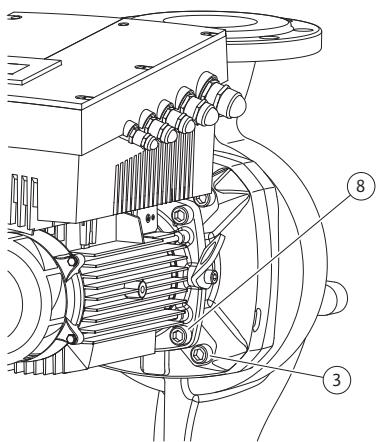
Fixarea optională a ansamblului motor cu rotor hidraulic
